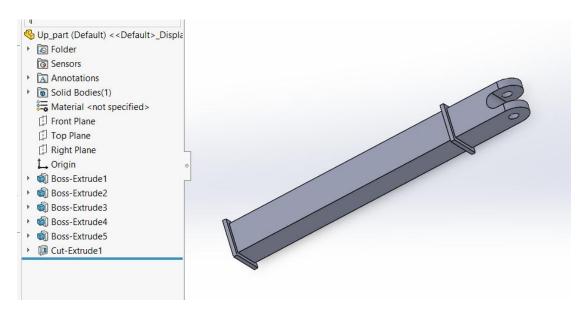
Основна мала рухома деталь принтера
